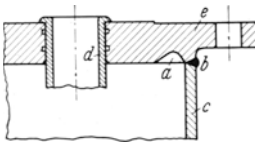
Angeschweißte abgesetzte Rohrwände.
